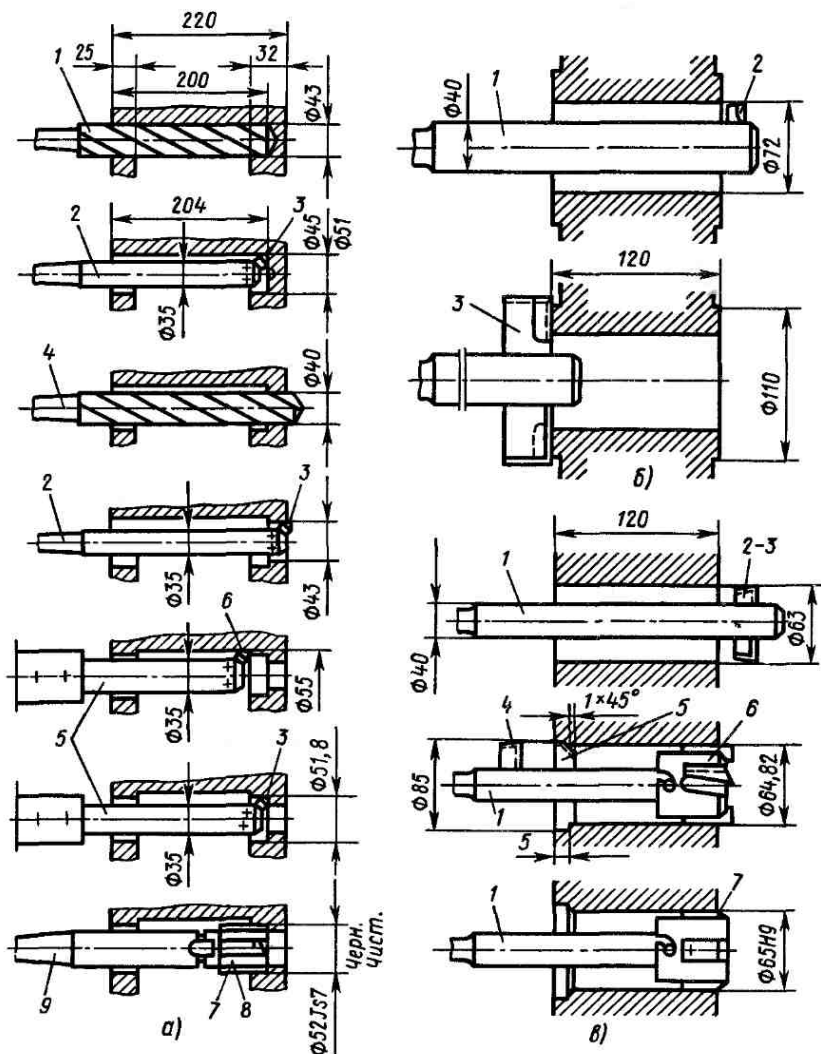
Обработка соосных отверстий $\varnothing 52Js7$
